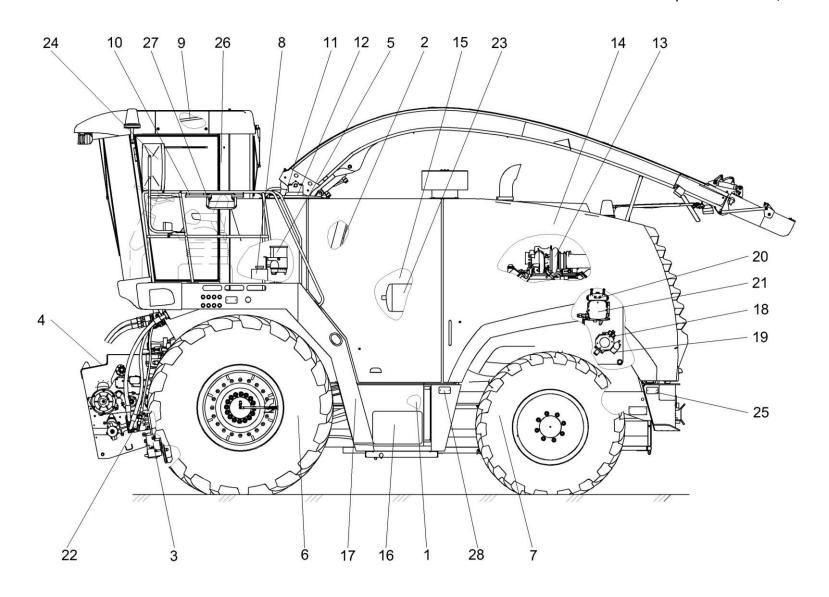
Измельчитель самоходный КВК 0100000-01 (вид слева)
